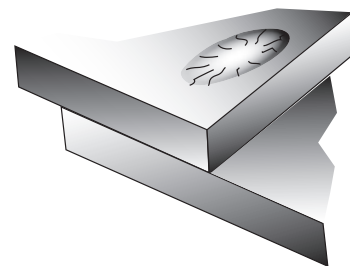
Joint typique pour le soudage à l'arc
